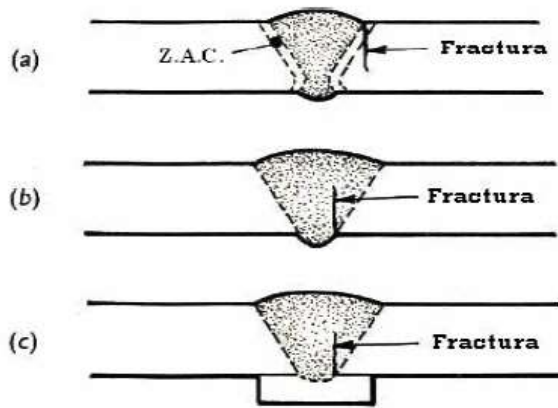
Modos típicos de fractura en soldadura a tope.
